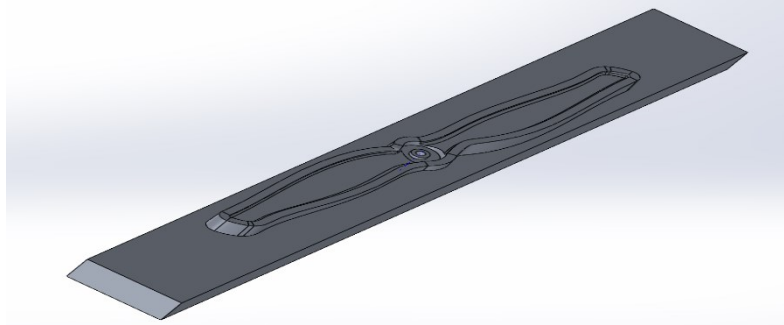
Diseño de base de aluminio de propela en SolidWorks
